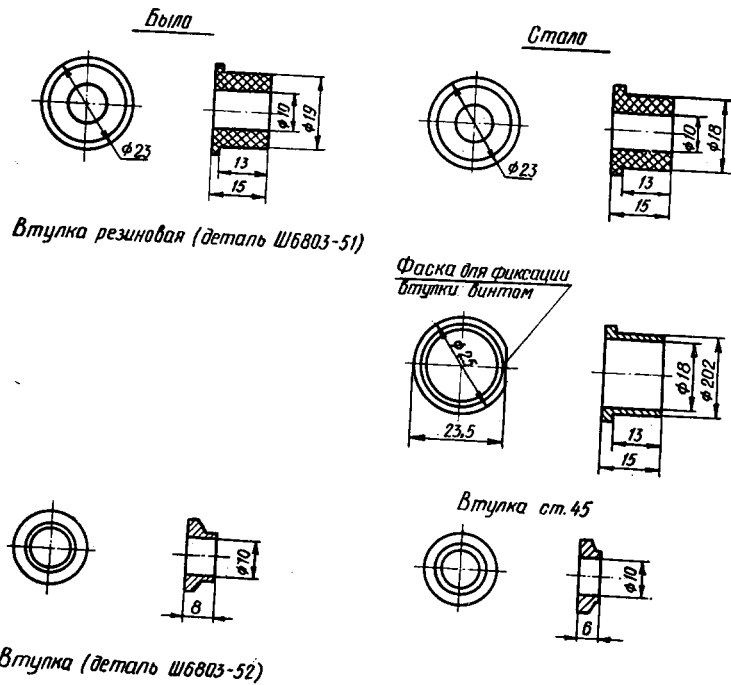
Доработка втулок Ш6003-51, Ш6803-52 и введение дополнительной стальной втулки (Ст. 45) в случае выработки корпуса всасывающего патрубка втулками Ш6803-51
